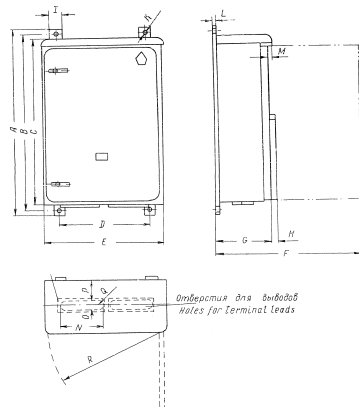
Габаритные размеры магнитных контроллеров серии ТБ
